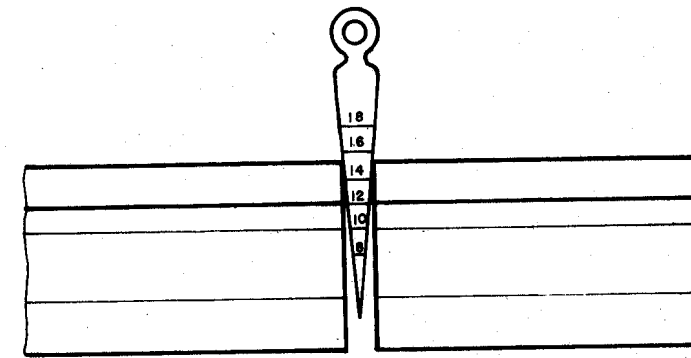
Medida de la separación entre extremos de carriles a soldar.
